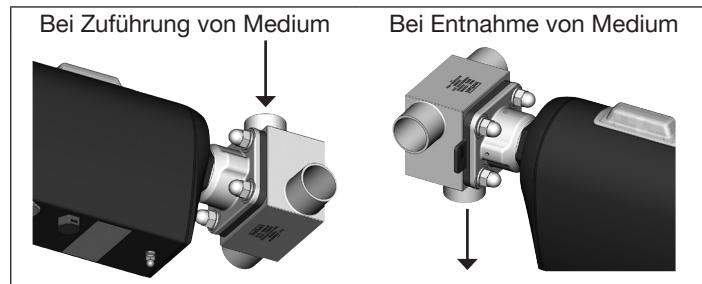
Einbaulage für T-Gehäuse, Typ 3364
